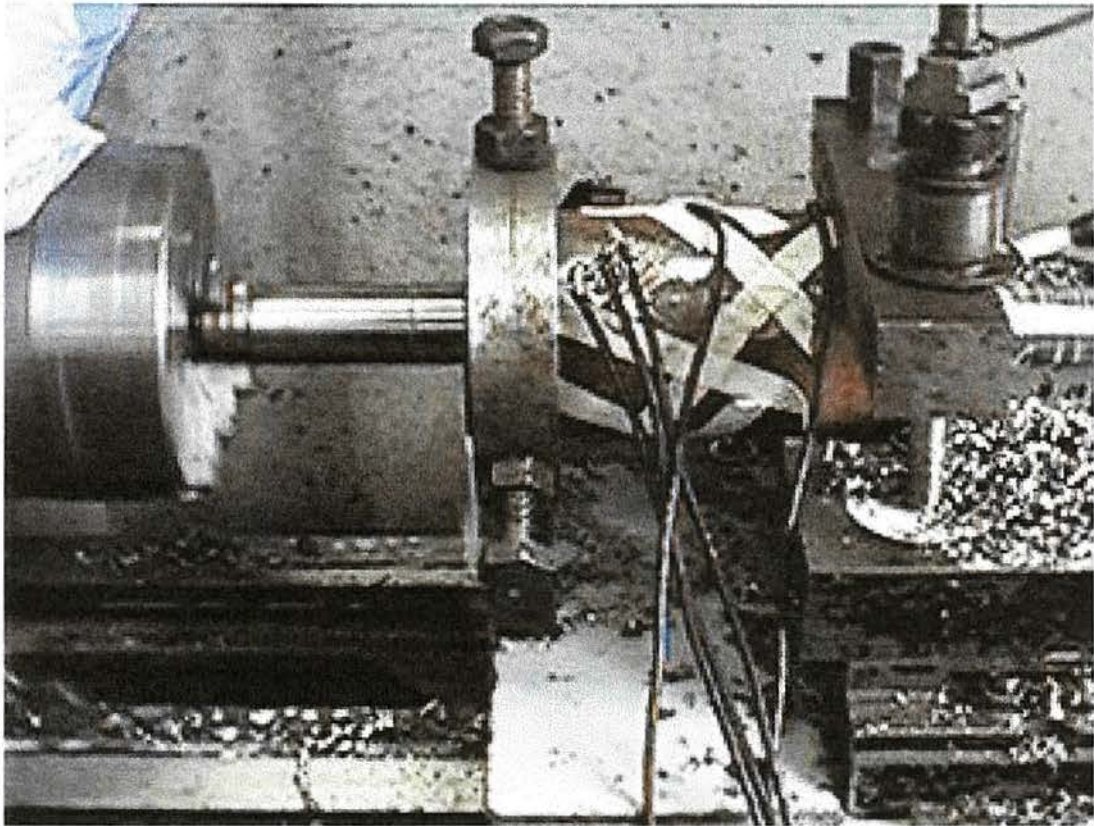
Detalhe de fixação do segmento de tubo no torno empregado na usinagem.
